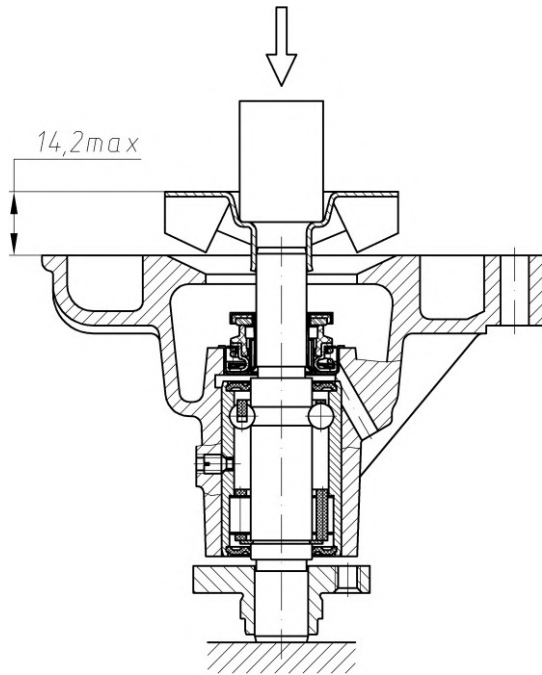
Aufpressen des Wasserpumpenlaufrads
